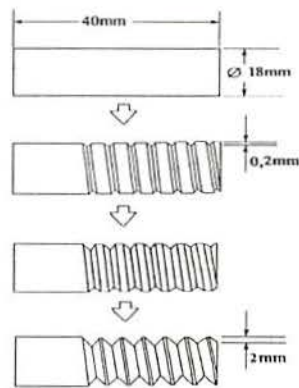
Esquema de usinagem dos corpos-de-prova com formato cilíndrico.
